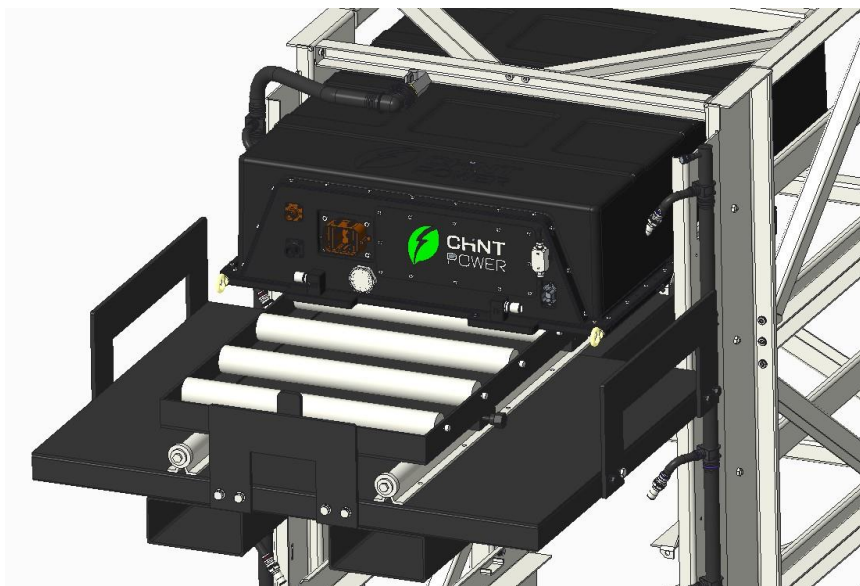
Coloque el paquete de baterías en la herramienta de elevación
